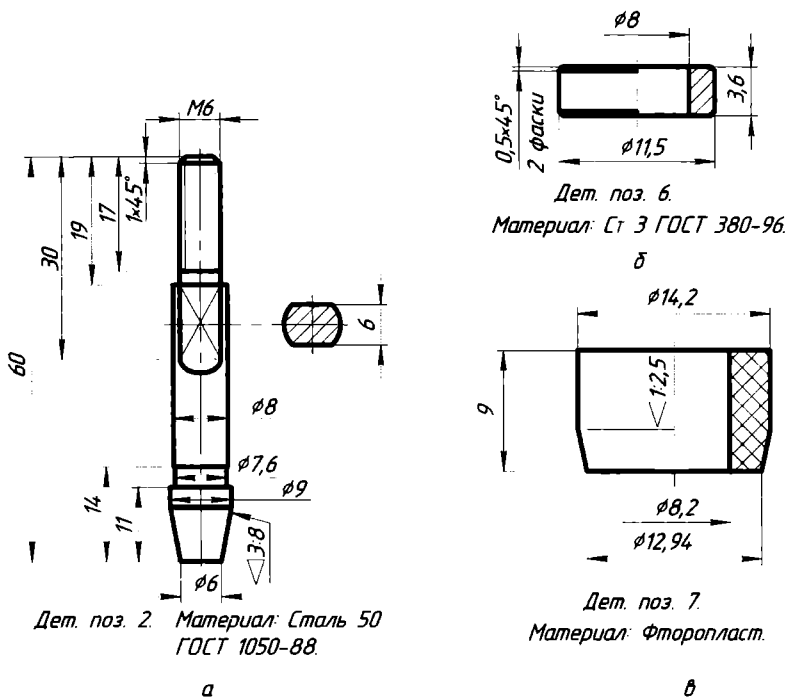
Чертежи: а — клапана; б — кольца; в — втулки уплотнительной
